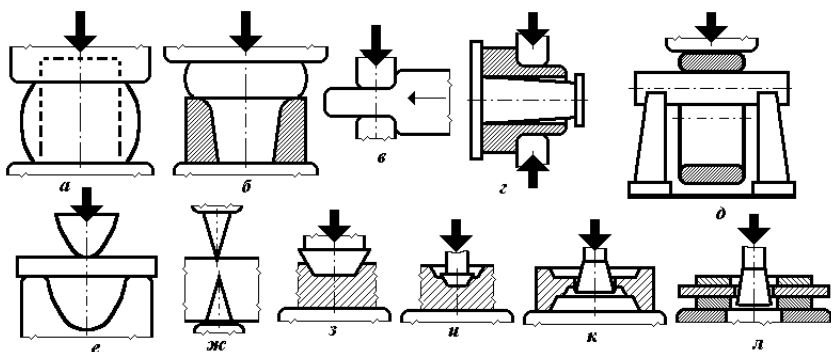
Основные операцииковки: а – осадка; б – высадка; в – протяжка; г – протяжка с оправкой; д – раскатка на оправке; е – гибка; жс – отрубка; з – прошивка неглубоких полостей; и – прошивка глубоких полостей; к – прошивка сквозных полостей; л – высадка с подкладкой; стрелками указаны направления действия силыковки.
